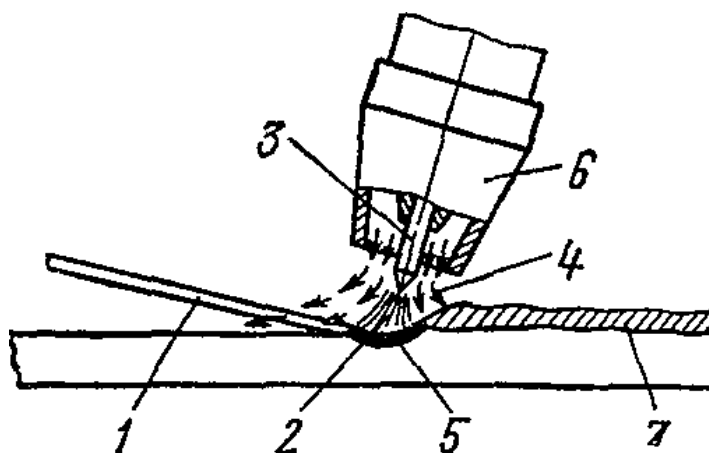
Схема ручной аргонодуговой сварки неплавящимся электродом.
